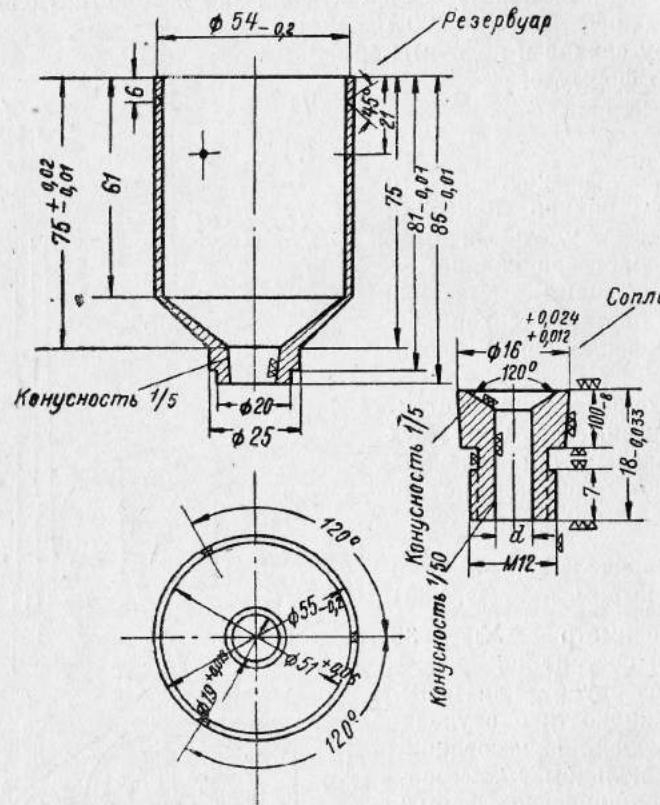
Корпус резервуара и сопло № 2 вискозиметра № 36.
